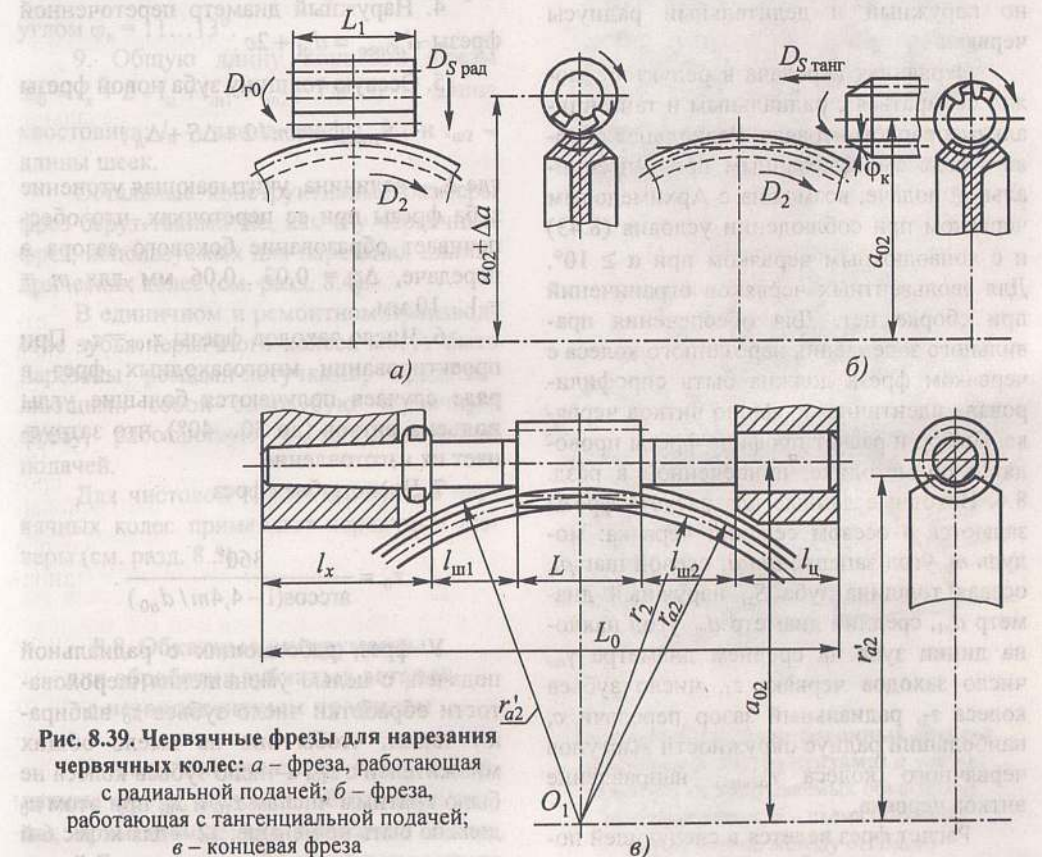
Червячные фрезы для нарезания червячных колес: а – фреза, работающая с радиальной подачей; б – фреза, работающая с тангенциальной подачей; в – концевая фреза
